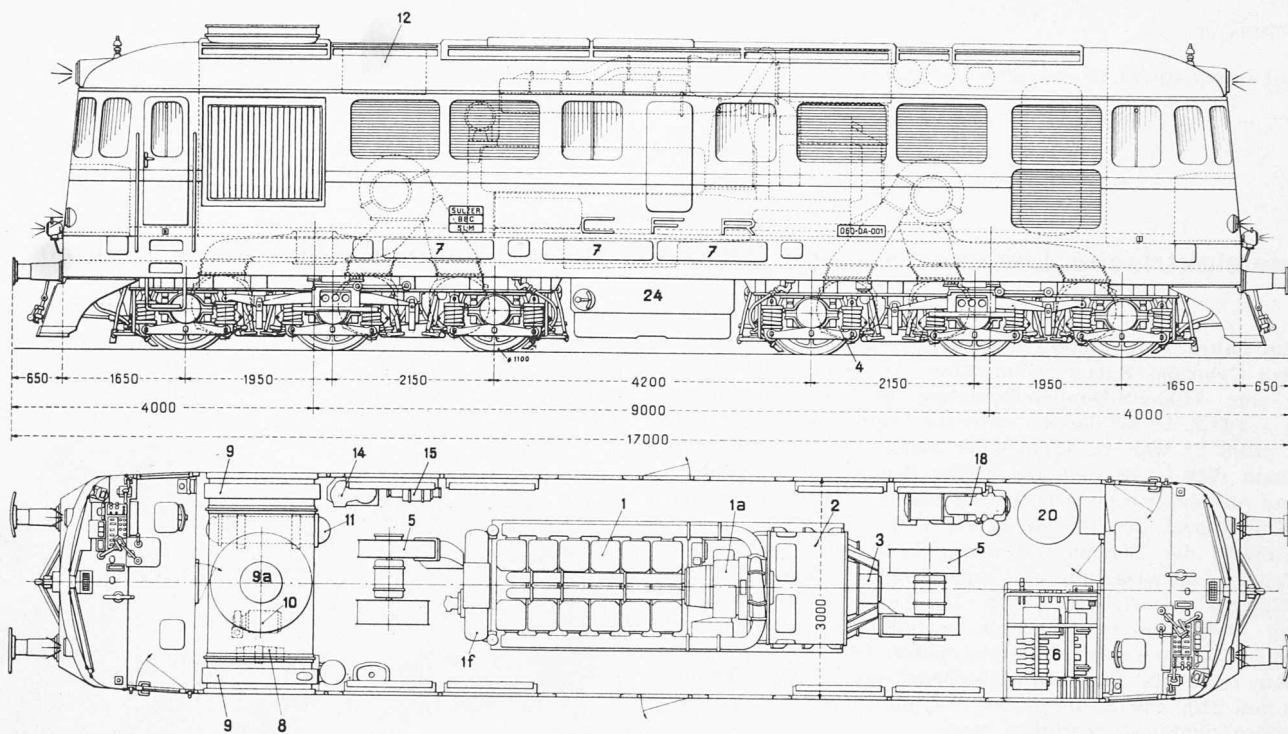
Ansicht und Grundriss der Lokomotive, 1:100
